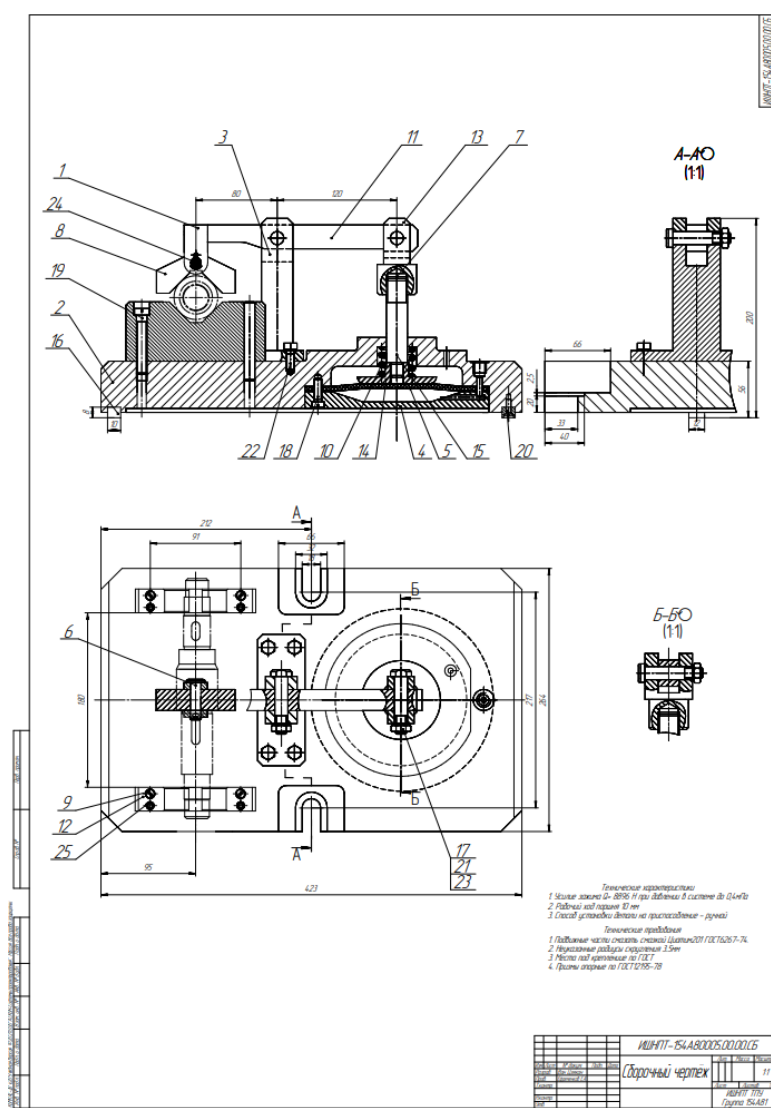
Сборочный чертеж приспособления приведен на формате А1
